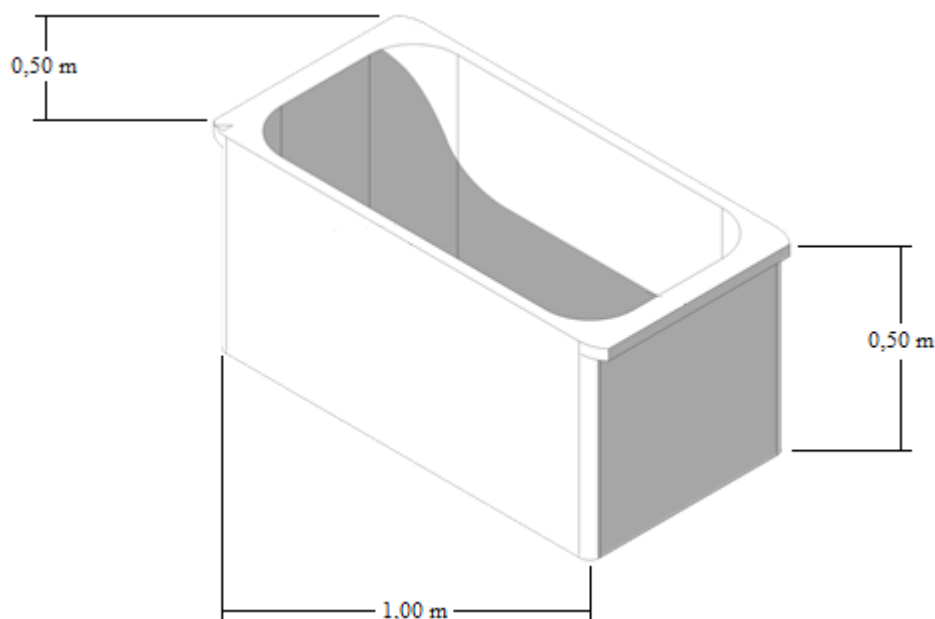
Vista isométrica del tanque acondicionador de quinua
